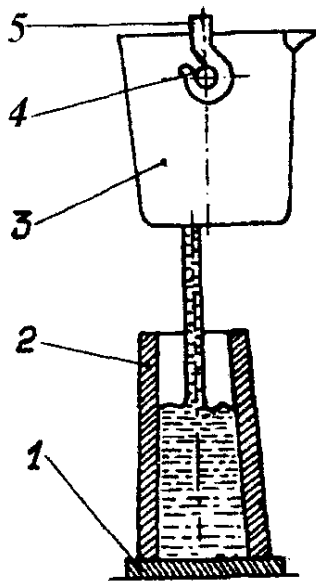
Розливання сталі у виливницю зверху [2]:
